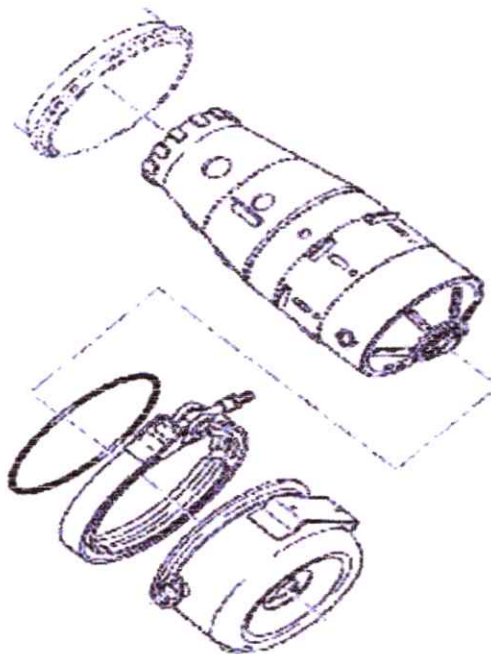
Chambre de combustion de l'APU GTCP 85 – 129
